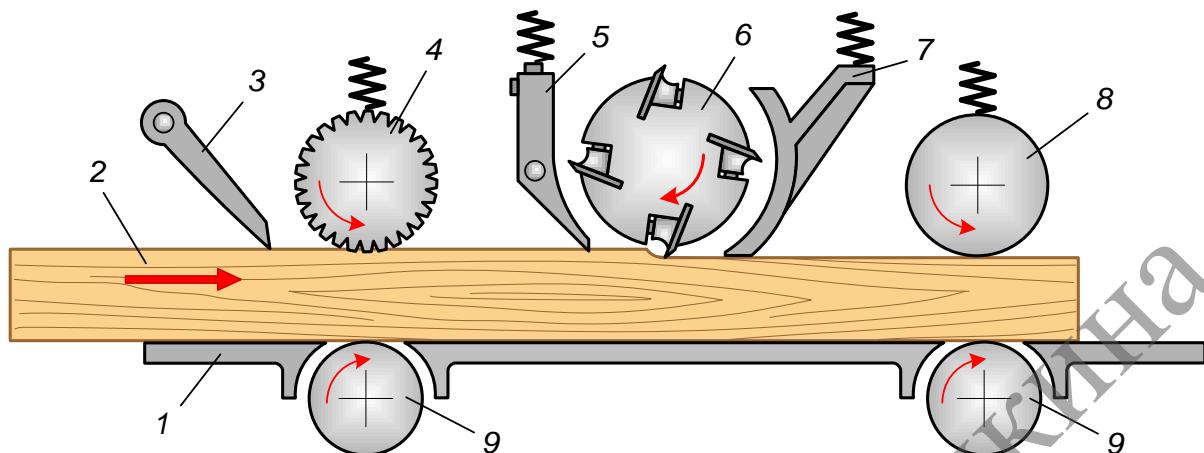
Схема устройства одностороннего рейсмусового станка
